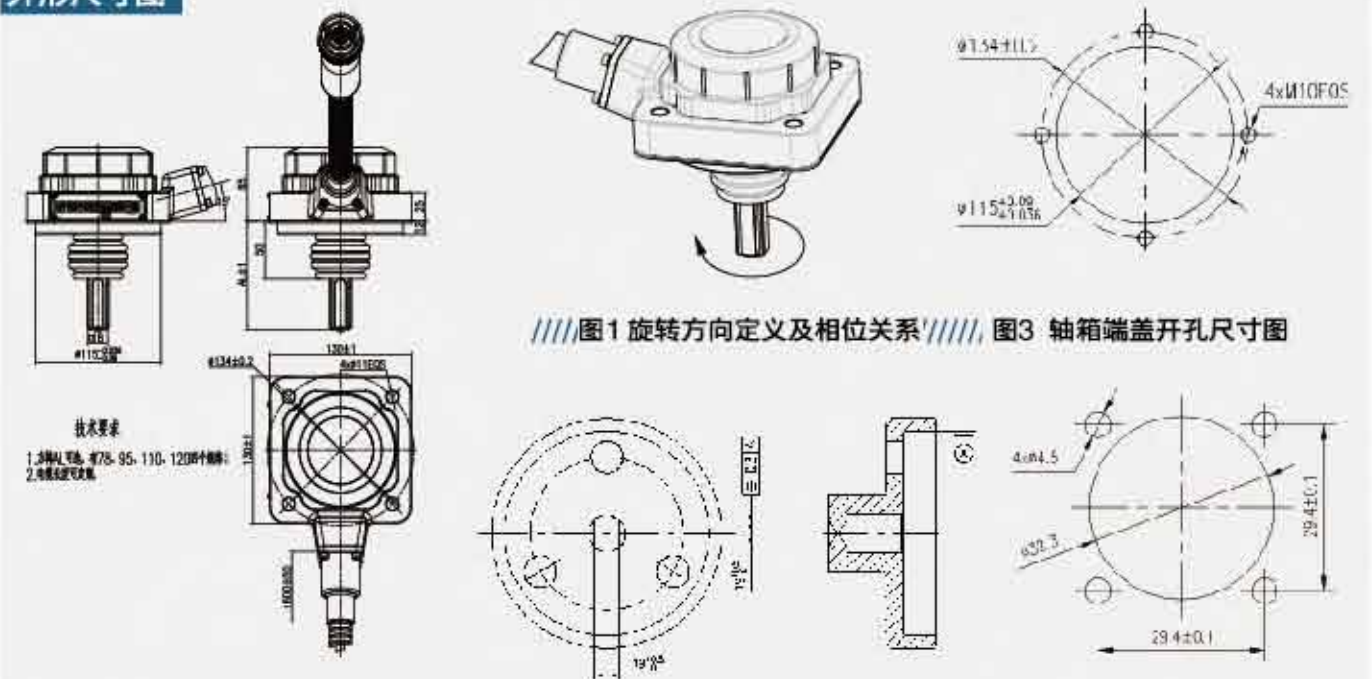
旋转方向定义及相位关系 图2 外形尺寸图 图3 轴箱端盖开孔尺寸图 图4 方孔套尺寸图 图5 JL5型电连接器插座安装开孔尺寸
